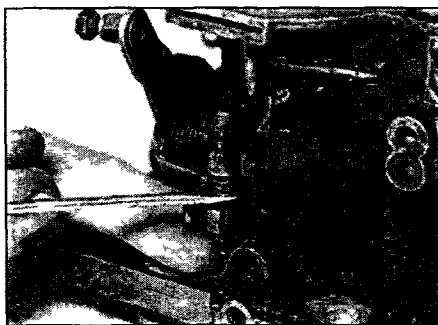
Часовой отверткой снимите подпружиненный конец тяги с рычага привода
